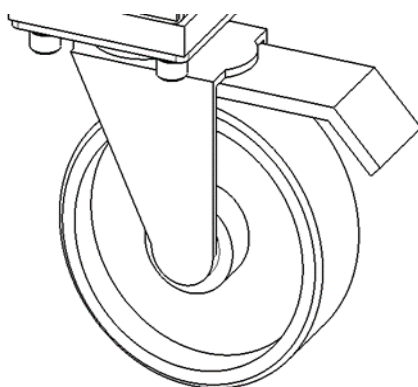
Схема устройства колесо поворотное с стопором
